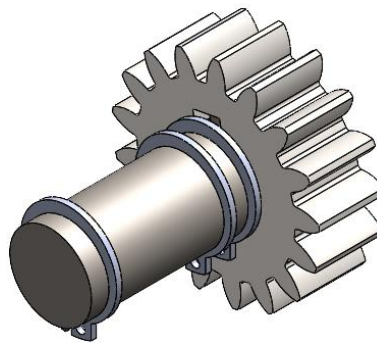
Ensamblaje CAD 3D de los componentes asociados al eje de entrada.
